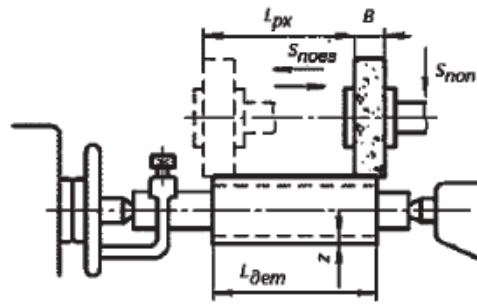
Схема круглого зовнішнього шліфування з поздовжньою подачею
